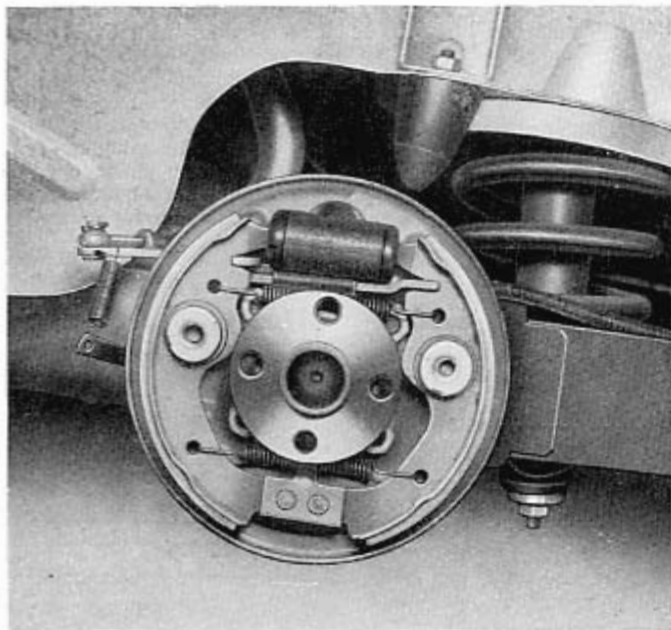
Plateau de frein de roue arrière droite, sans tambour.
